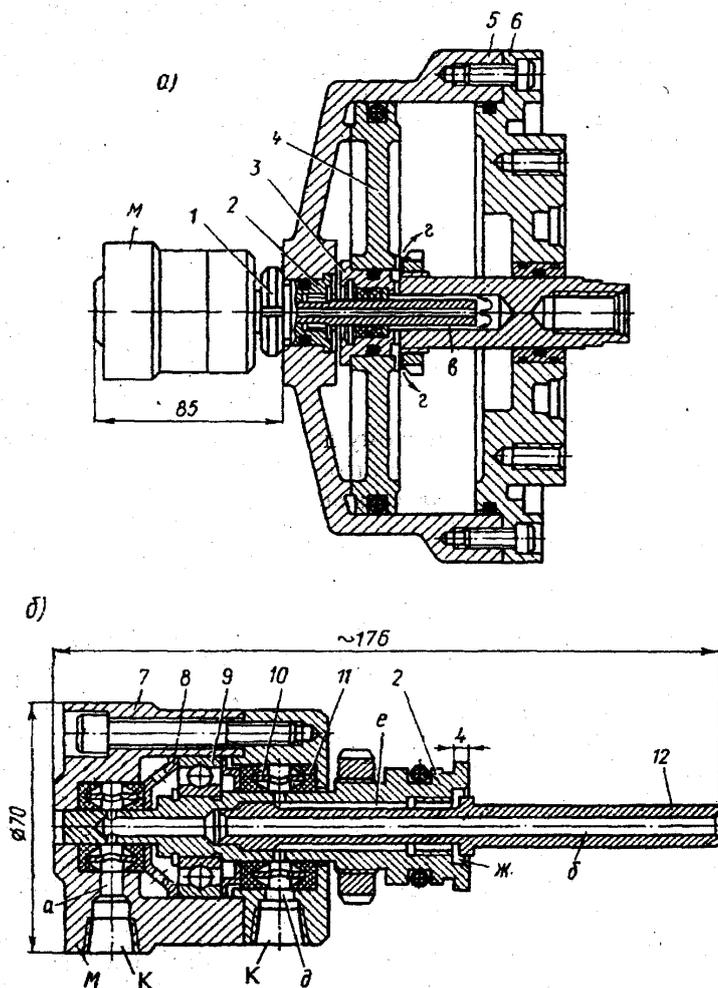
Вращающийся одинарный пневмоцилиндр (а) и муфта для подвода воздуха (б)
